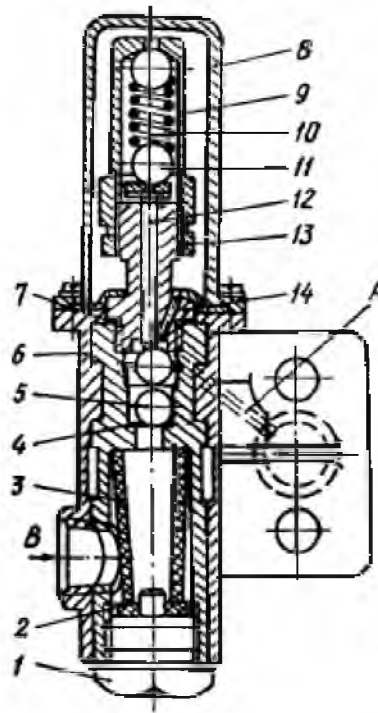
Регулятор тиску: А - канал, що з'єднує регулятор про розвантажувальний пристрій компресора; В - підведення повітря від ваз-задушливих балонів; 1 - корпус фільтра; 2 - ущільнювач фільтра; 3 - фільтр; 4 - пружина клапана; 5 - кульковий клапан; 6 - блок клапанів; 7 - регулювальні прокладки; 8 - кожух; 9 - ковпак регулювальний; 10 - пружина регулятора; 11 - куля пружини; 12 - шток клапана; 13 - контргайка; 14 - сідло клапана.
